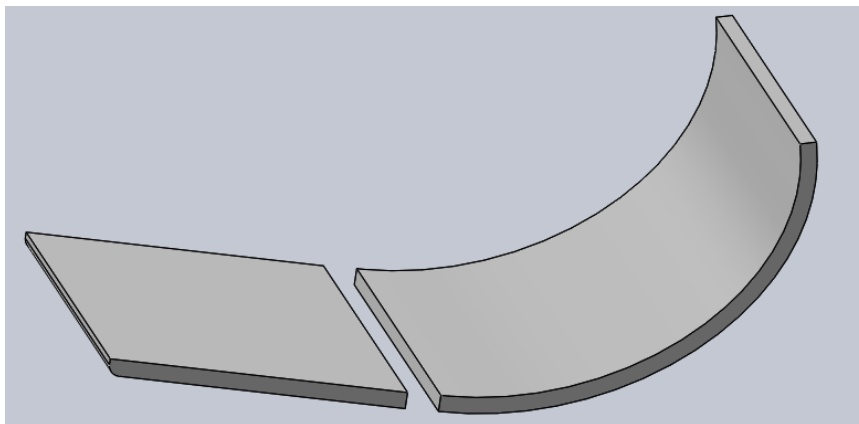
Vista explosionada del subensamblaje parte abajo cuerpo central. [2]
